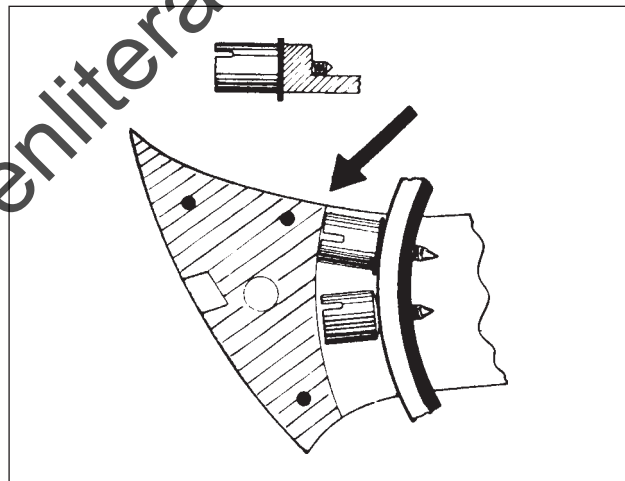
Eine Gefahr des Streifens ist gegeben, wenn die Scheibe oder die Schraube zu weit vorsteht.
